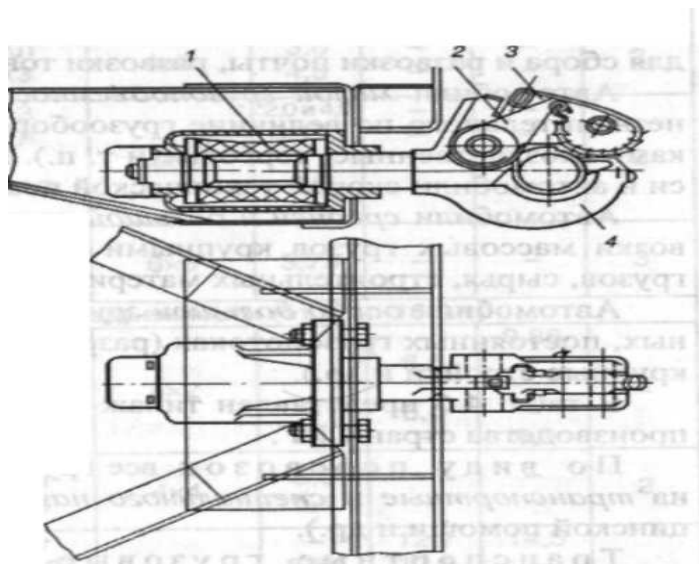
Тягово-цепное устройство автомобиля: 1 ~ упругий резиновый буфер; 2- защелка; 3- собачка; 4 - крюк
